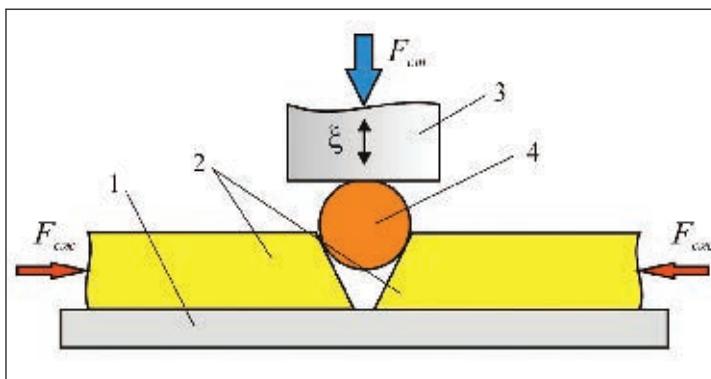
Схема ультразвуковой сварки полимерных листов с использованием присадочного материала: 1 — опора; 2 — свариваемые листы; 3 — волновод; 4 — пруток из присадочного материала
